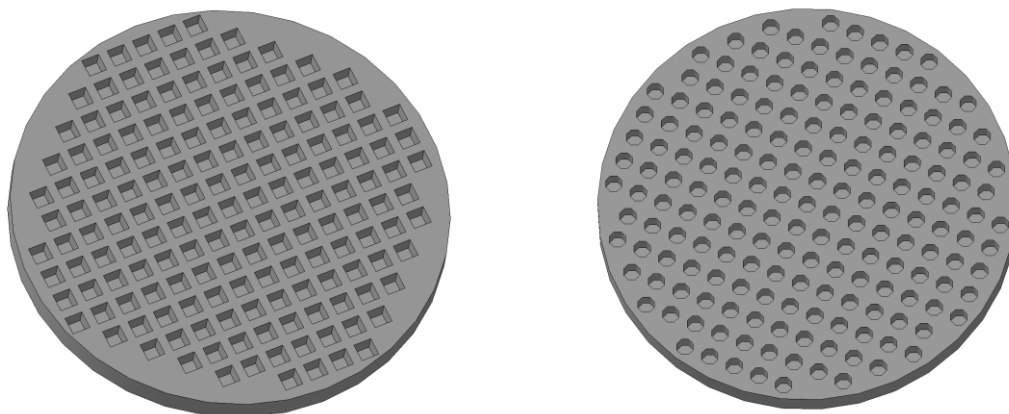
Композитные образцы матричных структур с цилиндрической (справа) и кубической (слева) ячейками
